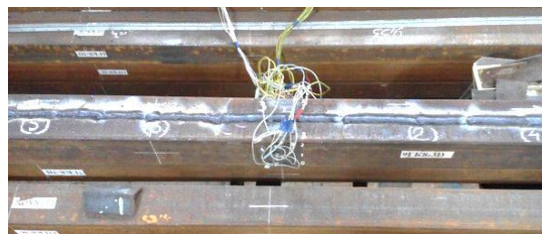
Правка элементов путем наплавки валиков сварных швов на растянутой стороне образцов
